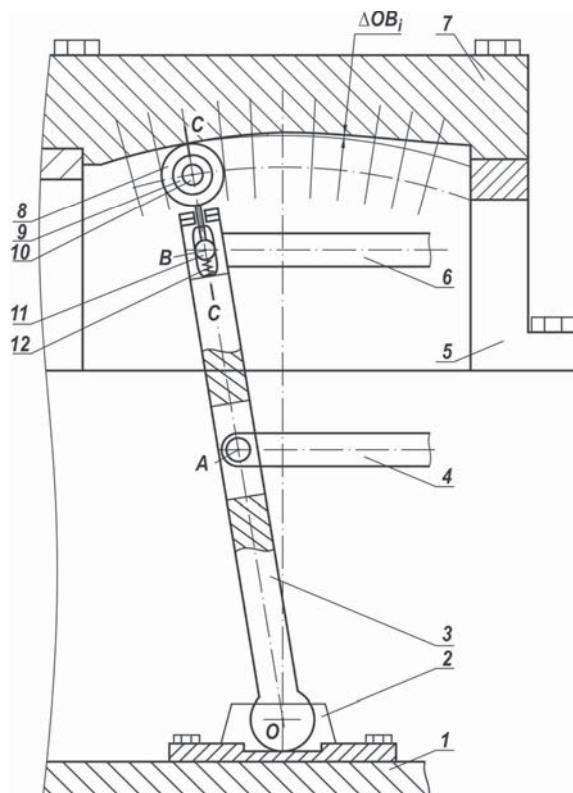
Механізм для регулювання довжини більшого плеча куліси: 1 – станина стана; 2 – основа куліси; 3 – куліса; 4 – тяга сепаратора кліті; 5 – стійка балки; 6 – тяга каретки кліті; 7 – калібрована балка; 8 – ролик; 9 – штир; 10 – вісь штиря та ролика; 11 – вісь тяги каретки кліті; 12 – пружина
